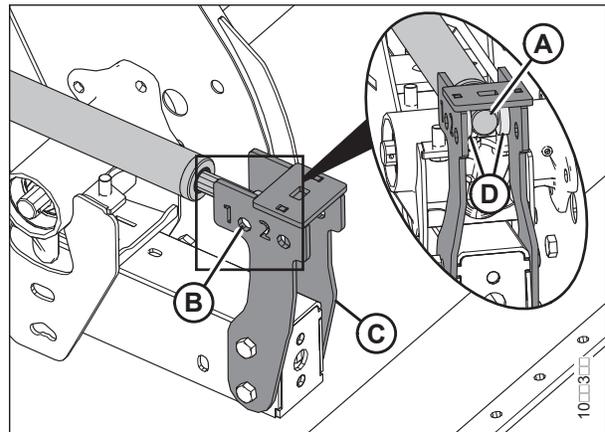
Rechter Haspel-Horizontalzylinder
